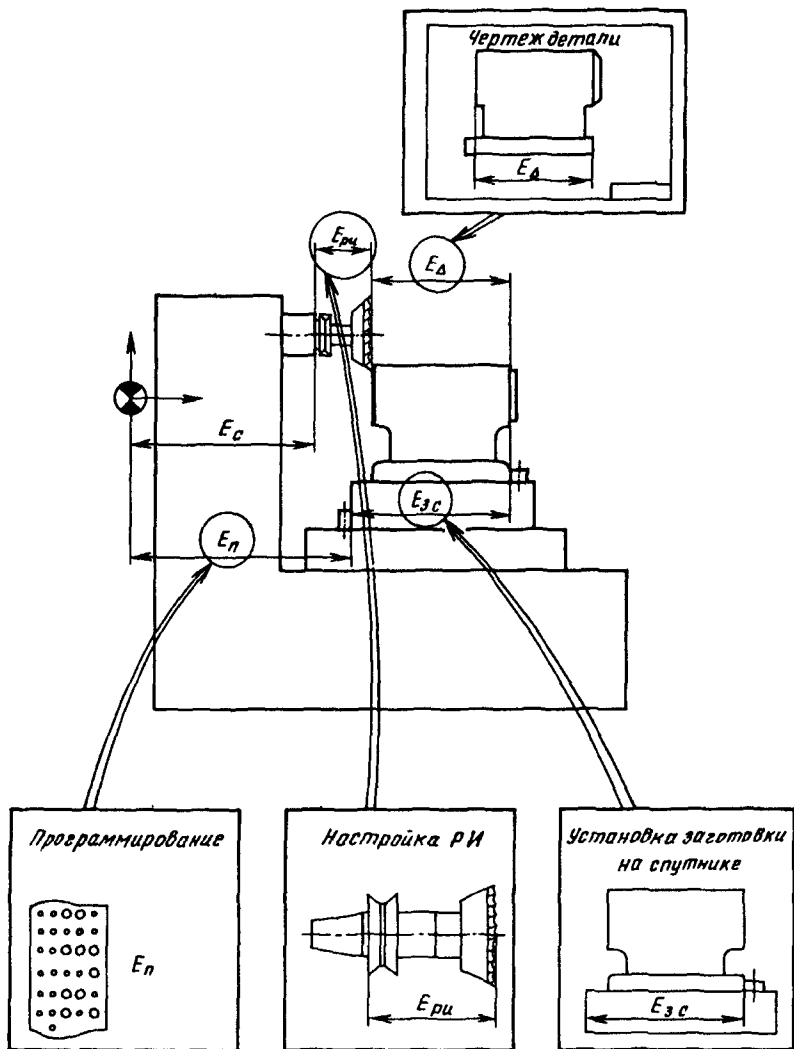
Схема согласования размеров в управляющей программе, настройке режущего инструмента, установки заготовки на спутник для автоматического получения требуемого размера детали
